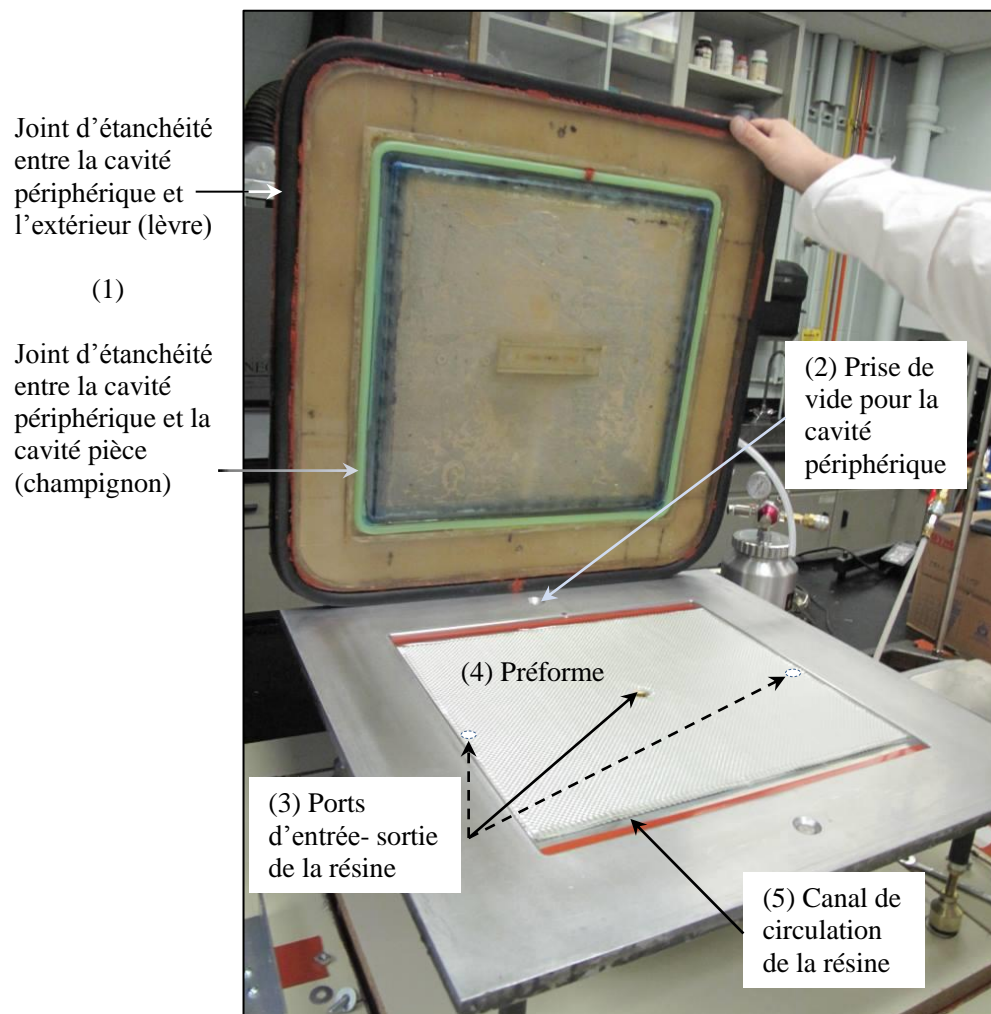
Photo du montage RTM-Light fabriqué.
